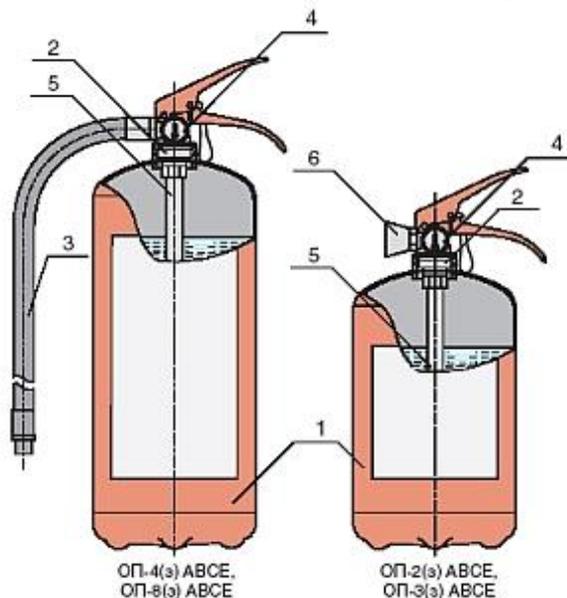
Принципиальная схема порошкового закачного огнетушителя: 1 – корпус; 2 – запорно-пусковое устройство; 3 – рукав; 4 – индикатор; 5 – сифонная трубка; 6 – сопло
